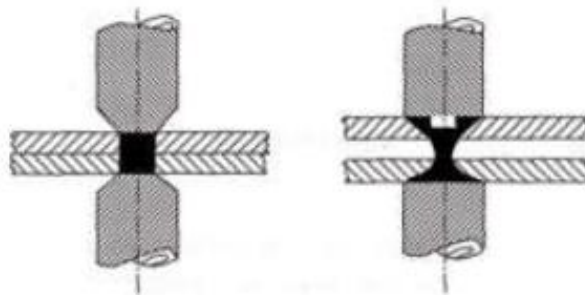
Soudage par point à gauche et par bossage à droite
